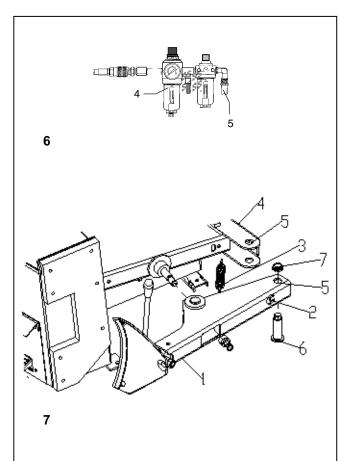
Montage du montant de la machine et de l'unité de conditionnement
